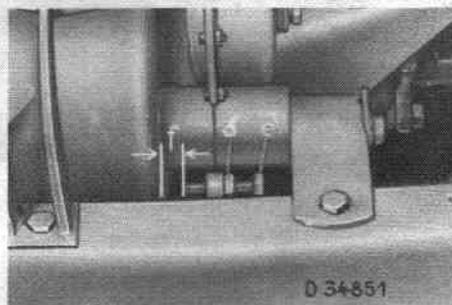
Réglage de la vis de l'embrayage du moteur
